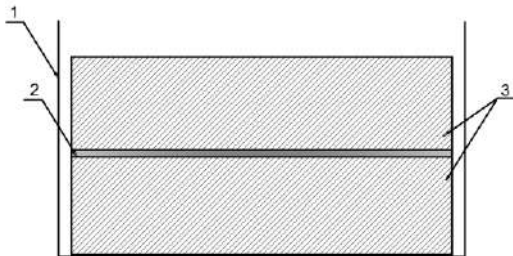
Схема поперечного перерізу шихтової заготовки: 1- невитратний короб; 2 - шар порошку TiO_2 ; 3 – шихтова заготовка.
